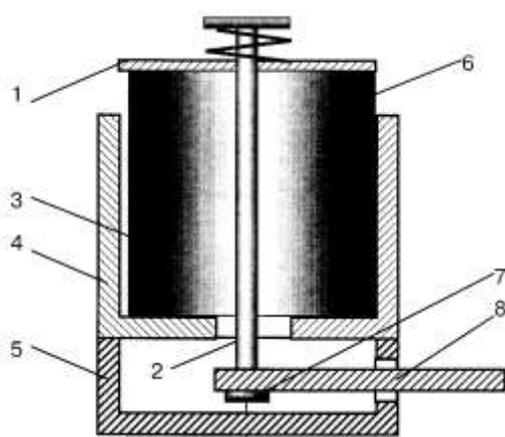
Конструктивная схема резинового виброизолятора подвесного типа: 1–крышка; 2–стержень; 3–зазор; 4–кожух; 5–корпус; 6–резиновый упругий элемент; 7–головка стержня; 8–кронштейн для крепления к опорной поверхности станка.
